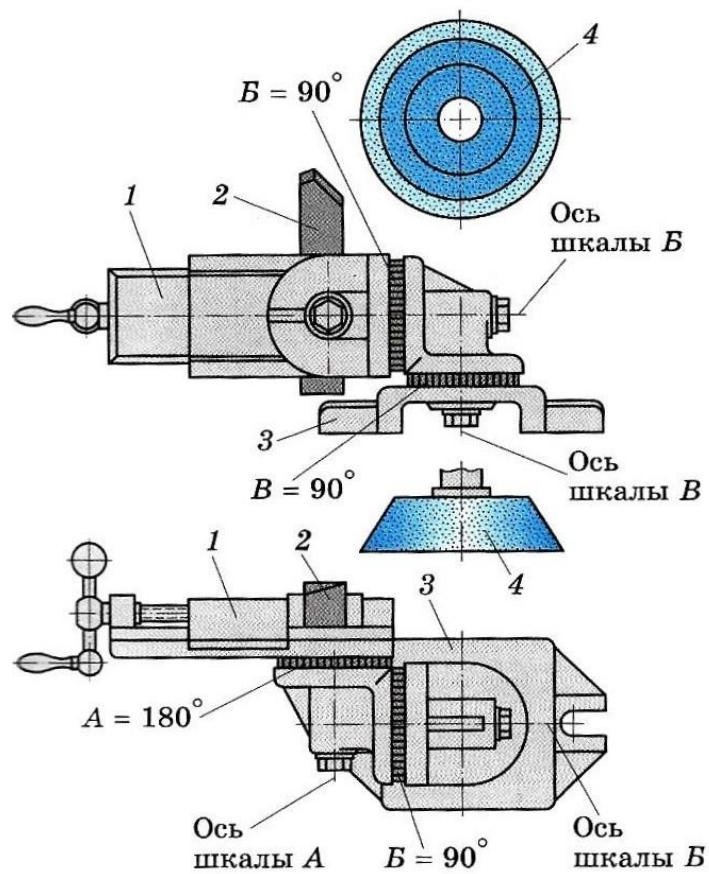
Поворотные 3-осевые тиски для заточки резцов
